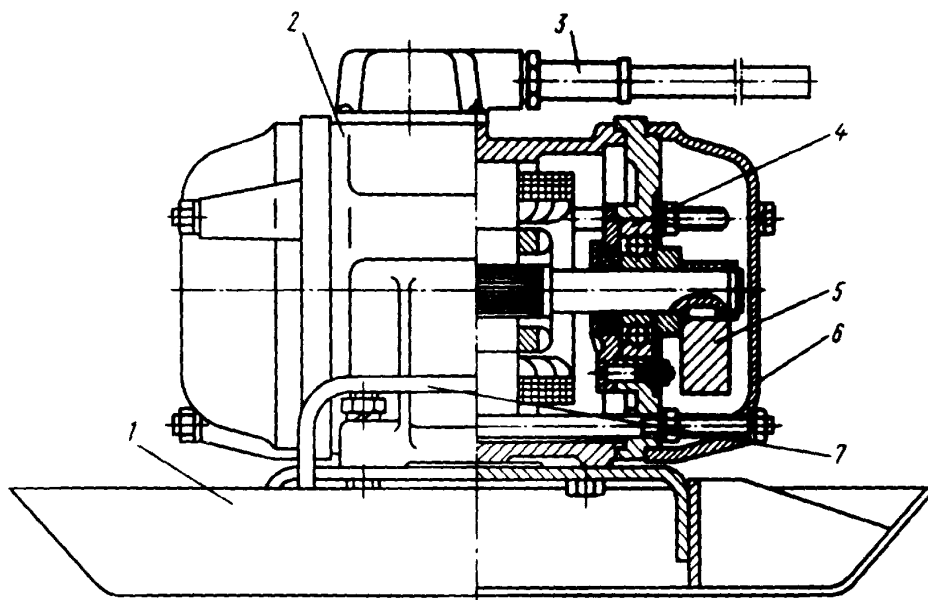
Поверхностный вибратор ИВ-91А: 1 – рабочая площадка; 2 – электродвигатель; 3 – токопроводящий кабель; 4 – подшипники; 5 – дебаланс; 6 – корпус; 7 – ручка
